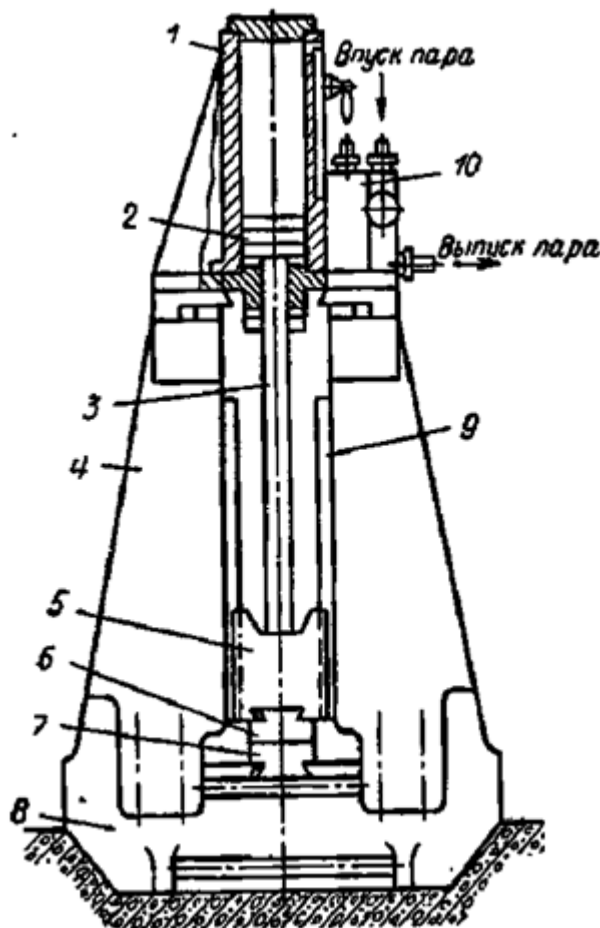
Схема паровоздушного штамповочного молота: 1 – цилиндр; 2 – поршень; 3 – шток; 4 – стойки; 5 – баба молота; 6 – верхний штамп; 7 – нижний штамп; 8 – шабот; 9 – направляющие; 10 – золотниковая коробка.
